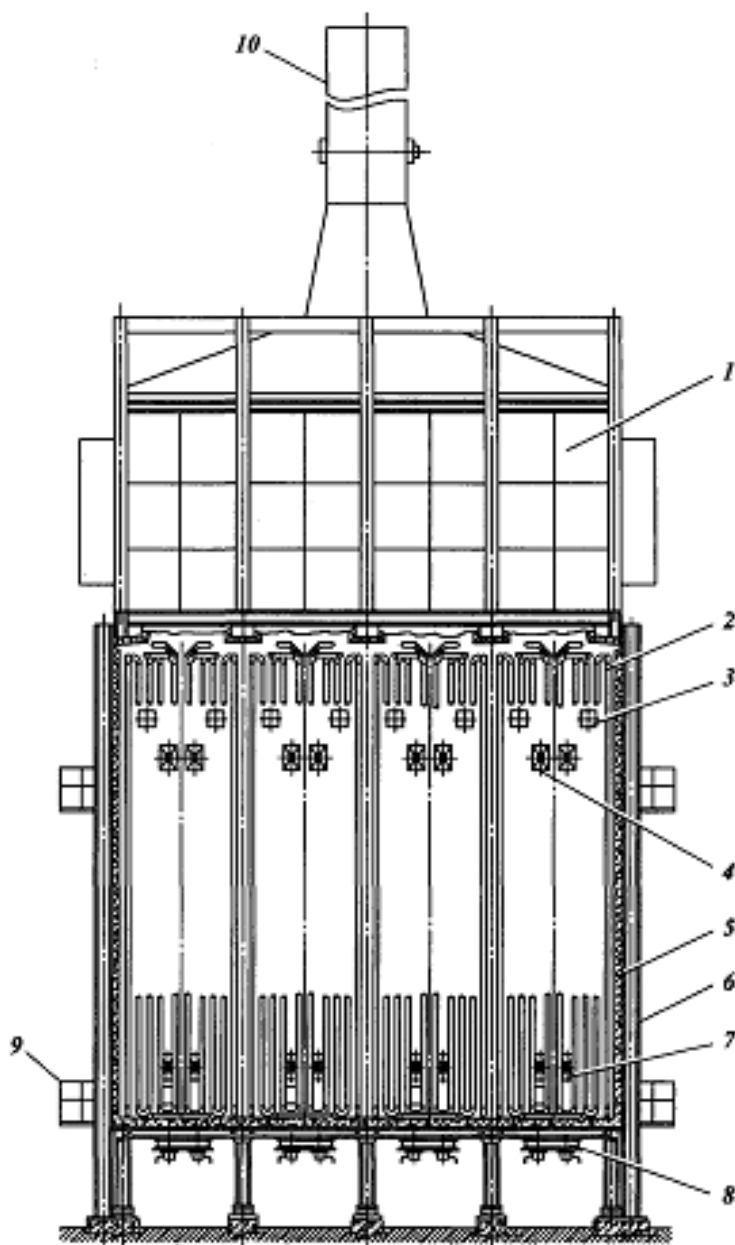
Конструкция трубчатой печи типа ВС:
